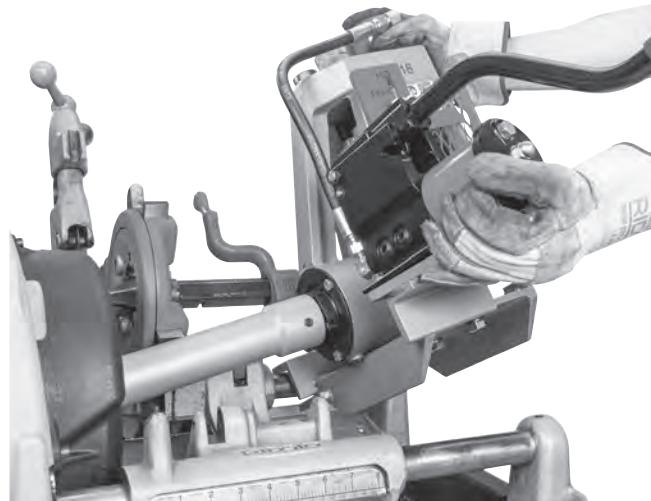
Nutrollmaschine 918 auf dem Sockel der Gewindeschneidmaschine 535
